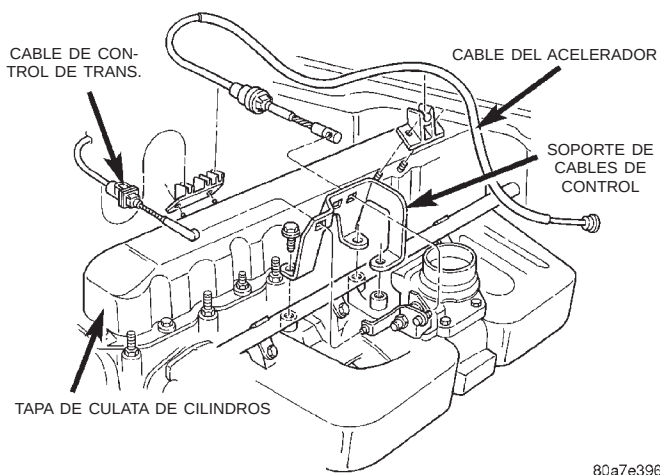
Tapa de la culata de cilindros del motor INSTALACION
